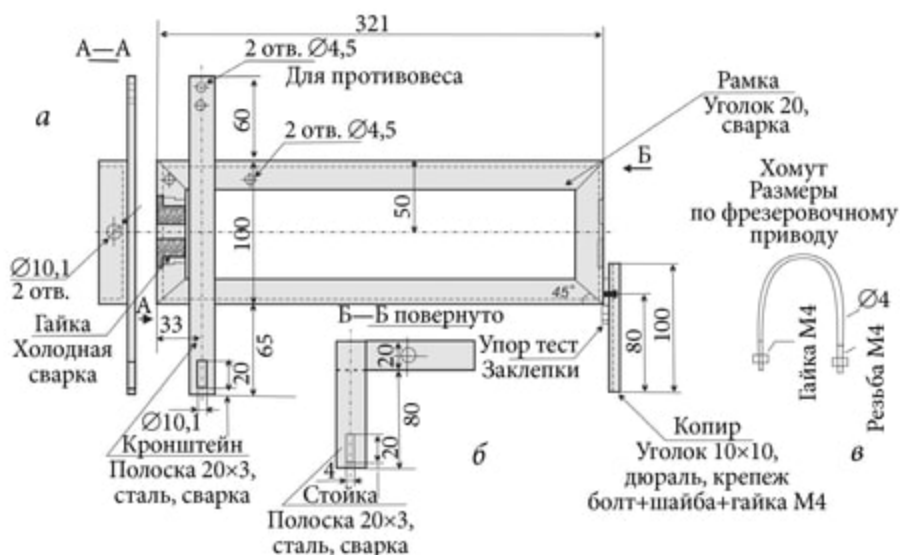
Металлическая рамка для крепления фрезеровочного привода и копия с отверстиями под приводной вал:
